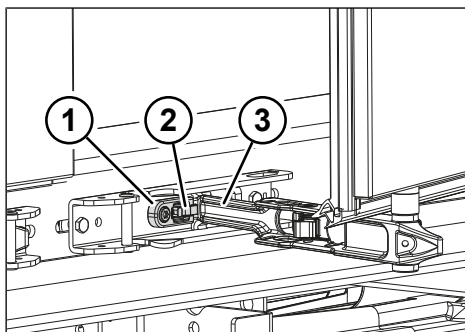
Leva per chiusura porte bloccata in posizione nel fissaporte
